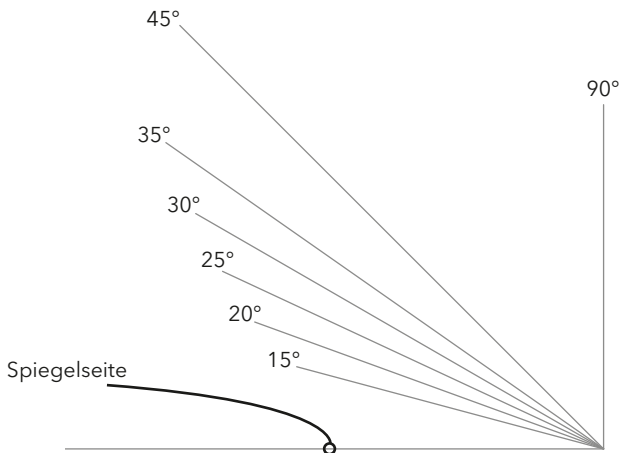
Häufige Schneidewinkel bei Holzbearbeitungswerkzeugen
